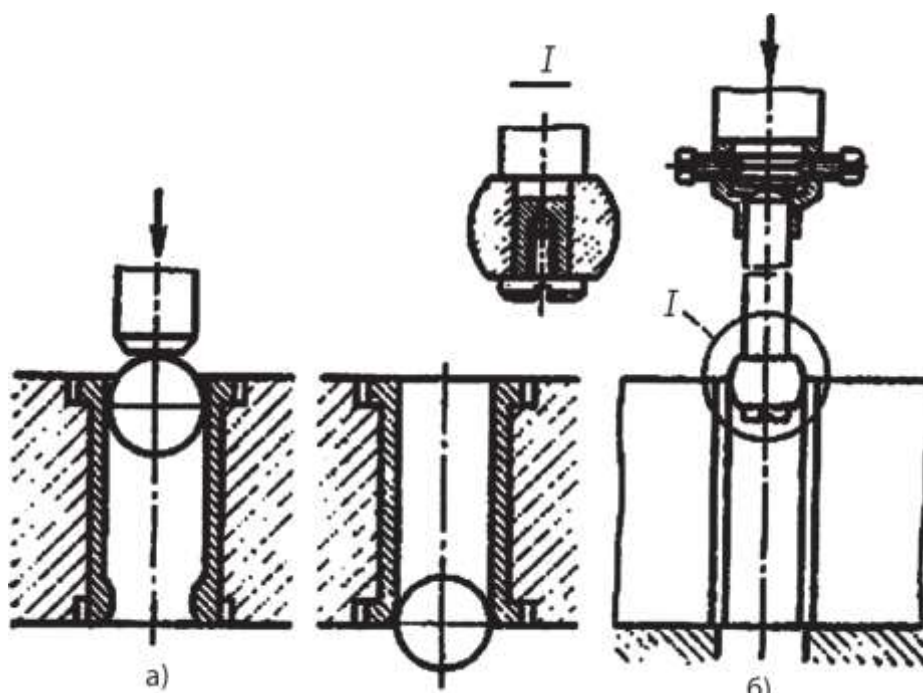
Калибровка подшипников-втулок после запрессовки: а — с отбортовкой; б — с созданием натяга
